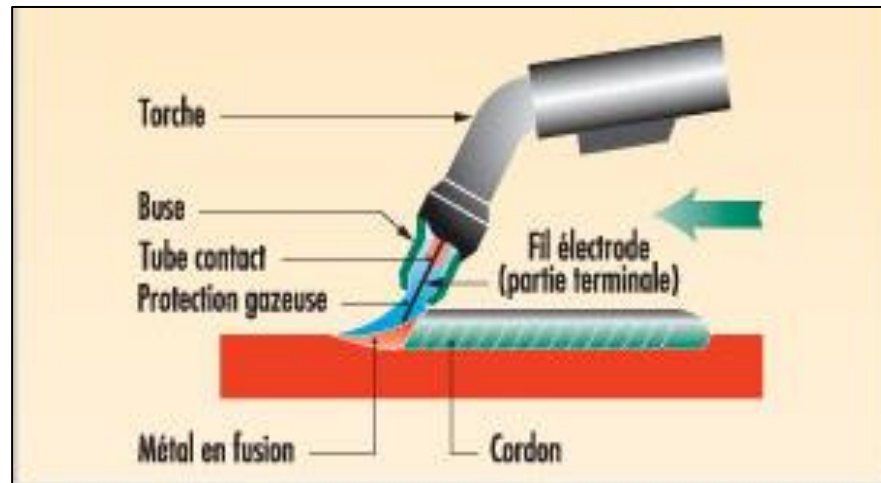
Principe de soudage MIG/MAG. [8]
